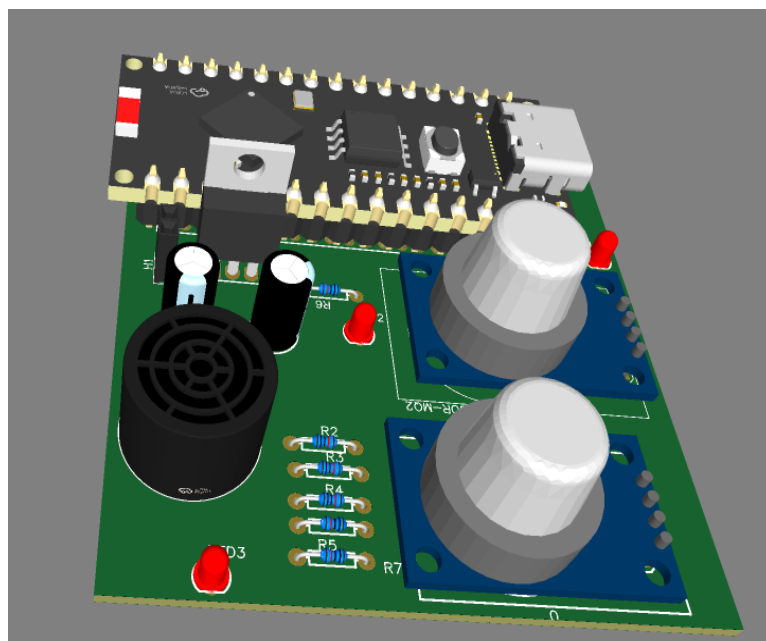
Vue 3D du Circuit Imprimé (PCB)
